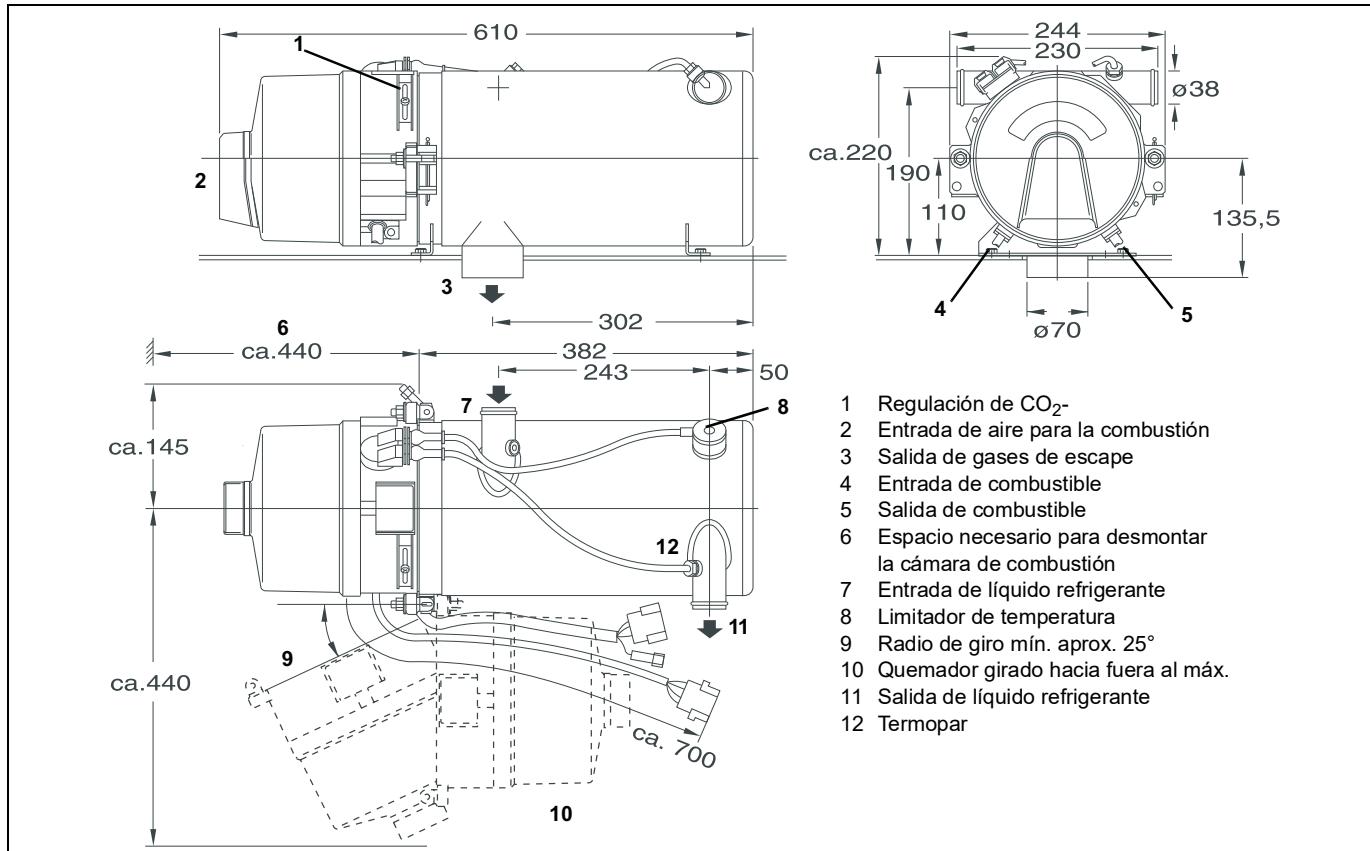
Dimensiones del calefactor Thermo 230 / 300 / 350 (montaje horizontal)
